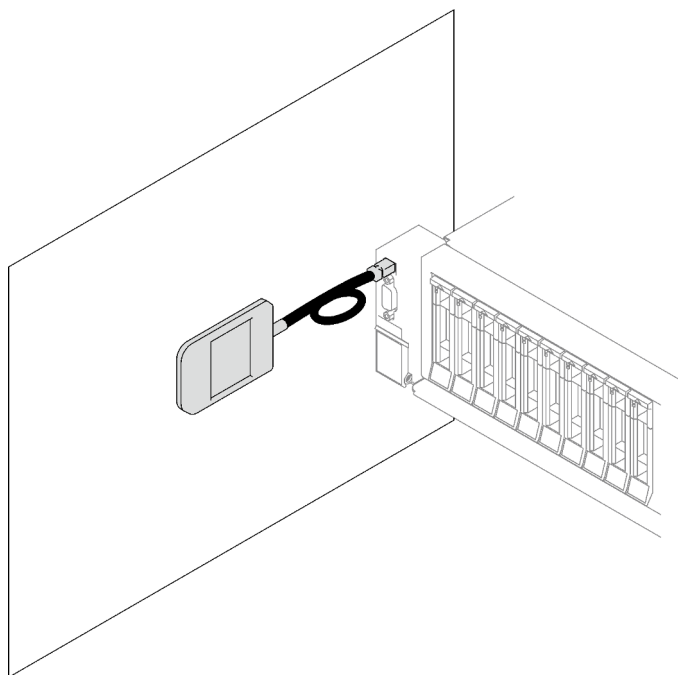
Befestigen des externen Diagnosegeräts an einer Metalloberfläche
